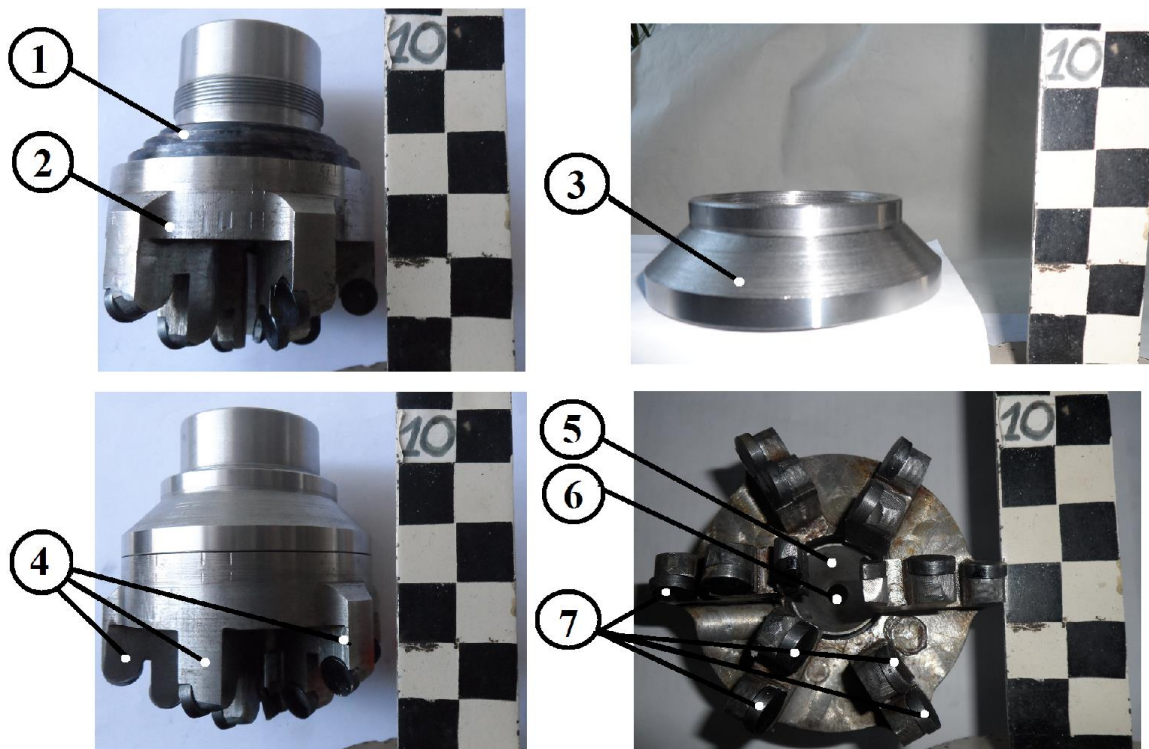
Різець кавітаційний 1 – корпус; 2 – магніти; 3 – кожух; 4 – ріжучі кромки; 5 – дифузorz кавітатора; 6 – промивний канал; 7 – твердосплавні вставки
